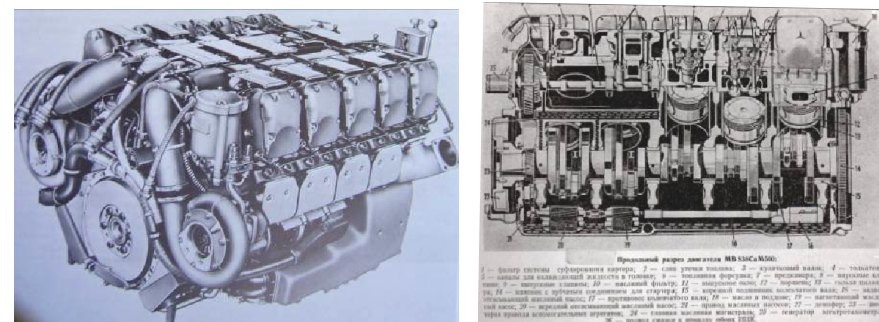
Общий вид (а) и разрез (б) двигателя MB838CaM500
